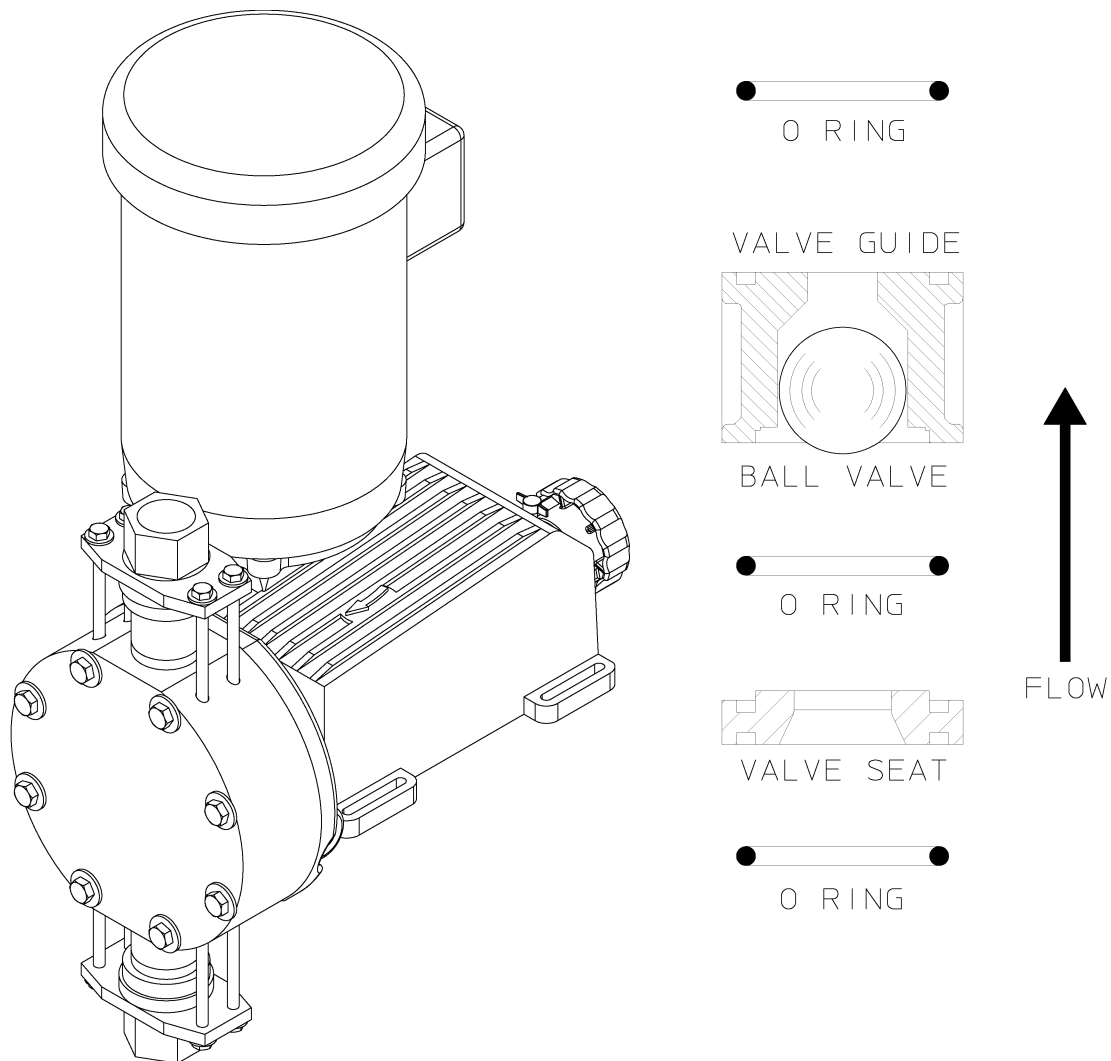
, Válvulas selectoras DC5 y 6, estructura metálica
